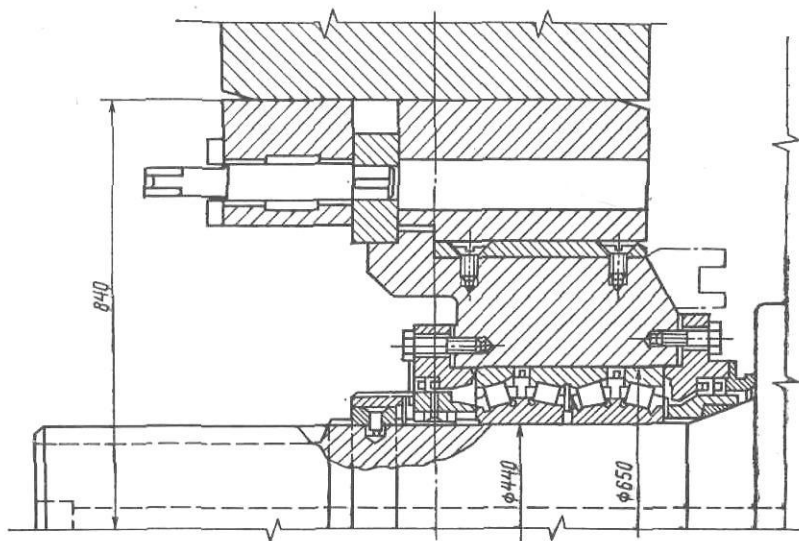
Установка рабочего валка четырехвалкового стана 2800 для прокатки дюралюминия на роликовых конических подшипниках
